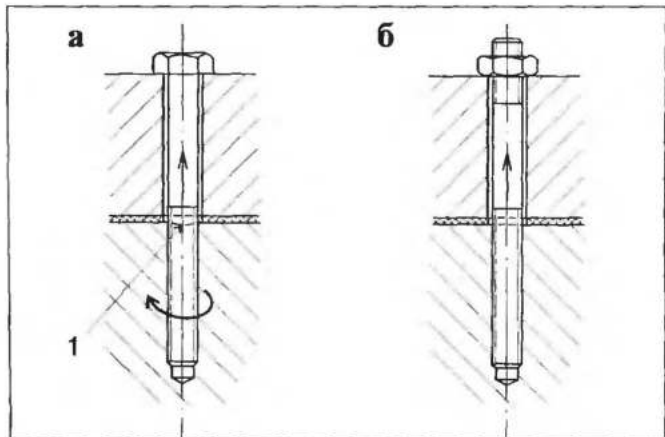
Замена болта на шпильку в случае прохождения трещины через резьбовое отверстие:
